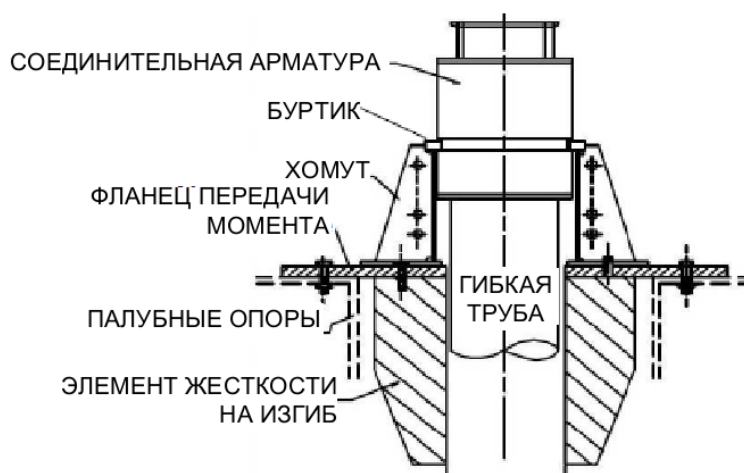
Устройство для передачи нагрузок с хомутом и буртиком, подпалубные брусы
